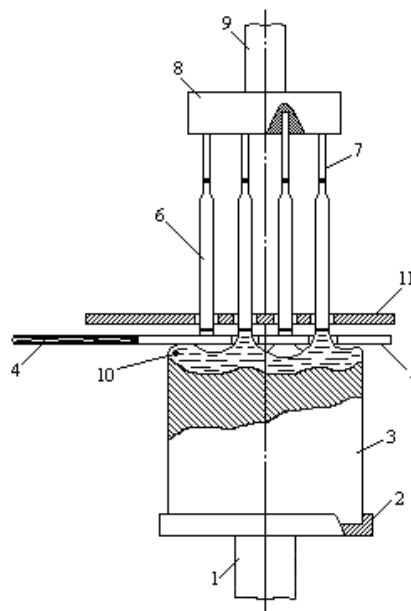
Схема группового выращивания прутков-подложек: 1 – нижний шток; 2 – держатель исходной заготовки; 3 – исходная заготовка кремния – пьедестал; 4 – токоподвод индуктора; 5 – высокочастотный индуктор для создания расплава; 6 – выращиваемые прутки-подложки; 7 – затравочный кристалл; 8 – держатель затравочных кристаллов; 9 – верхний шток; 10 – зона расплава; 11 – короткозамкнутый виток
